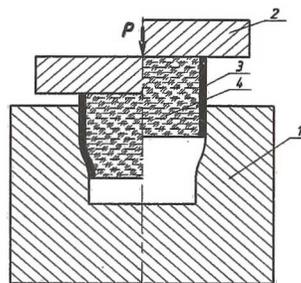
Штамп для обжима трубчатой заготовки с использованием ледяного стержня
